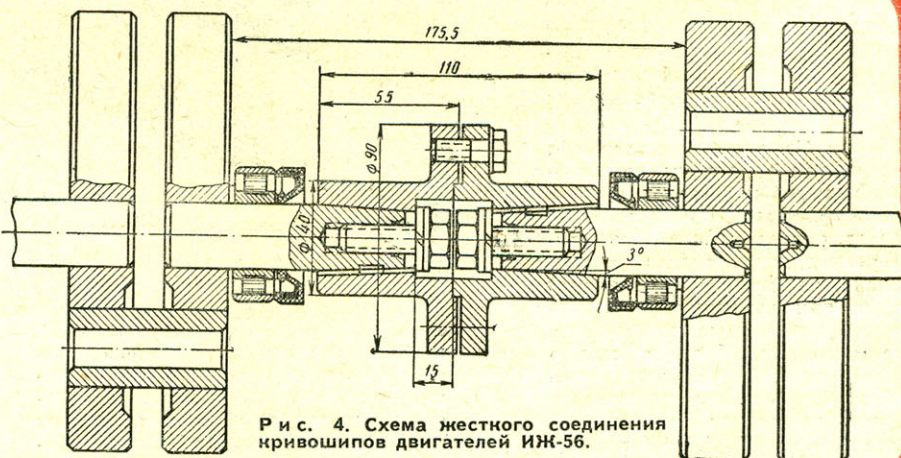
Схема жесткого соединения кривошипов двигателей ИЖ-56.
